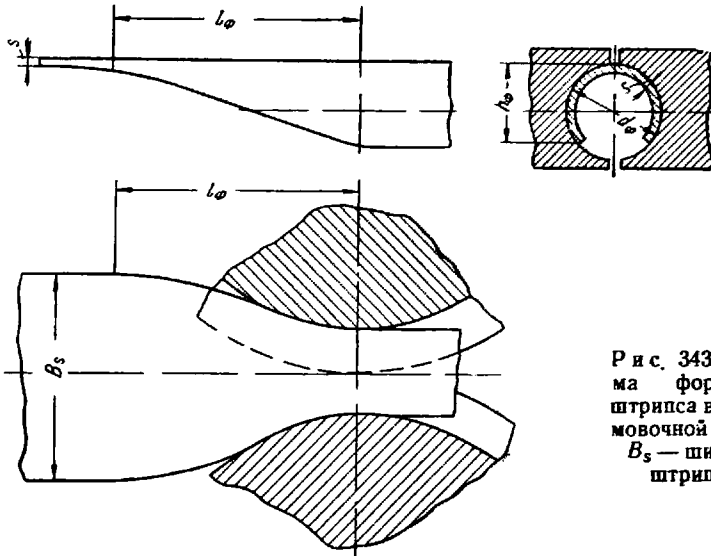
Схема формовки штрипса в формовочной клетке B_s — ширина штрипса
